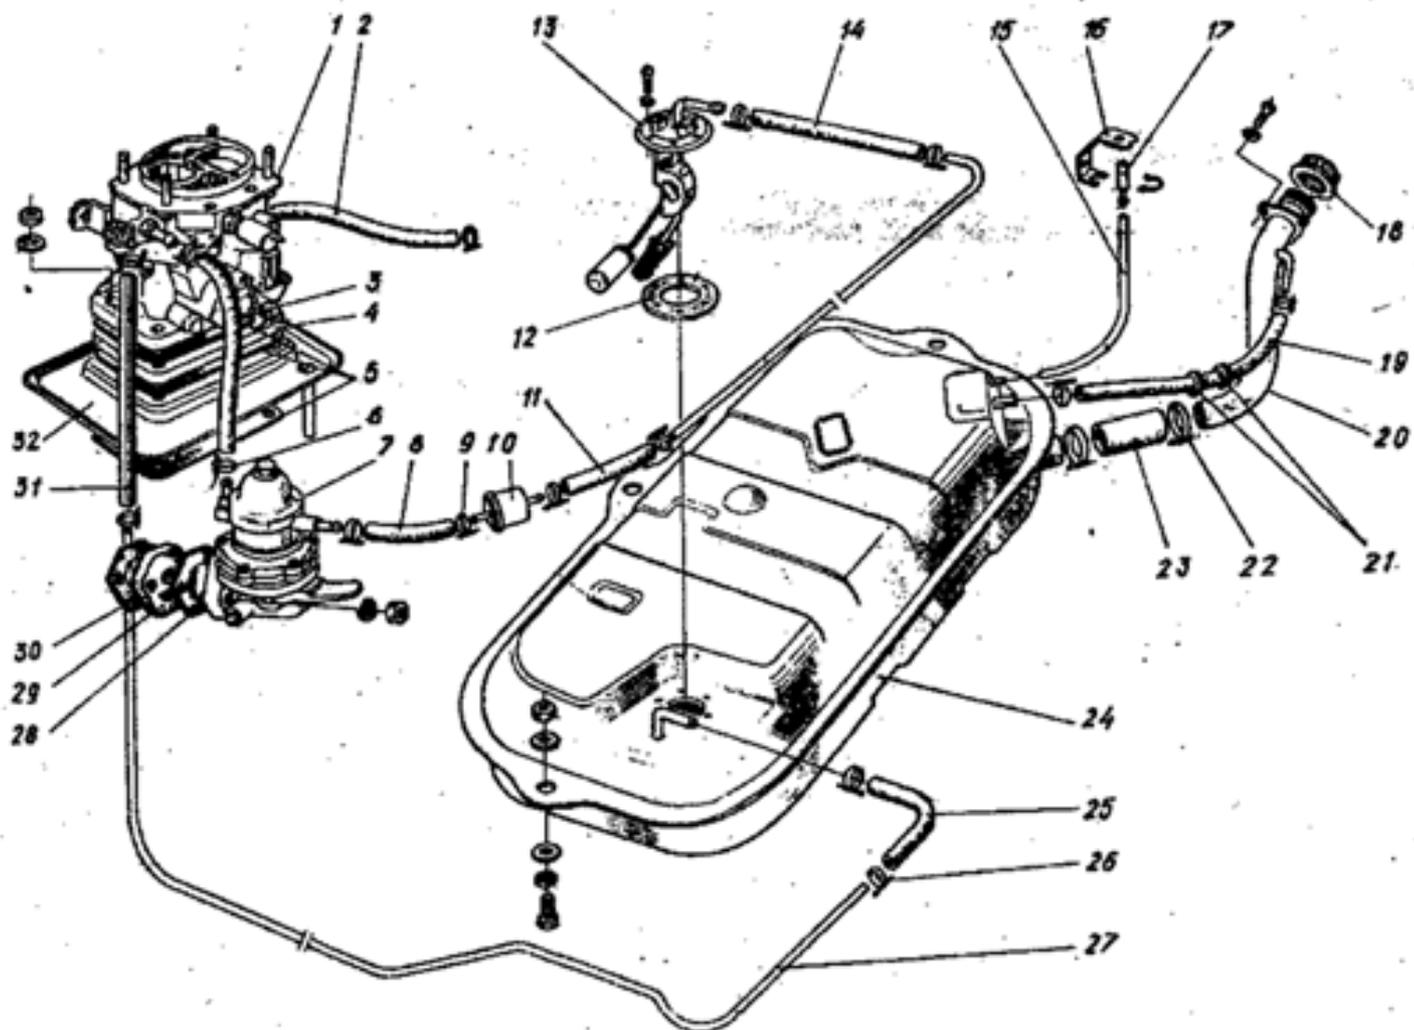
Детали системы питания (карбюратор 21081-1107010): 1 - карбюратор; 2 - шланг к вакуум-корректору; 3 - шланг подачи топлива к карбюратору; 4 - прокладка; 5 - прокладка; 6, 9, 22, 26 - хомуты; 7 - насос топливный; 8, 11 - шланги подачи топлива к топливному насосу; 10 - фильтр тонкой очистки топлива; 12 - прокладка датчика; 13 - датчик уровня бензина; 14 - шланг соединительный; 15 - вентиляционная трубка; 16 - кронштейн; 17 - наконечник вентиляционной трубки; 18 - пробка топливного бака; 19 - шланг воздушный; 20 - трубка наливная; 21 - втулка; 23 - шланг наливной трубки; 24 - топливный бак; 25 - шланг соединительный; 27 - трубка рециркуляции; 28 - прокладка уплотнительная; 29 - прокладка; 30 - прокладка регулировочная; 31 - шланг трубки рециркуляции; 32 - топливосборник
